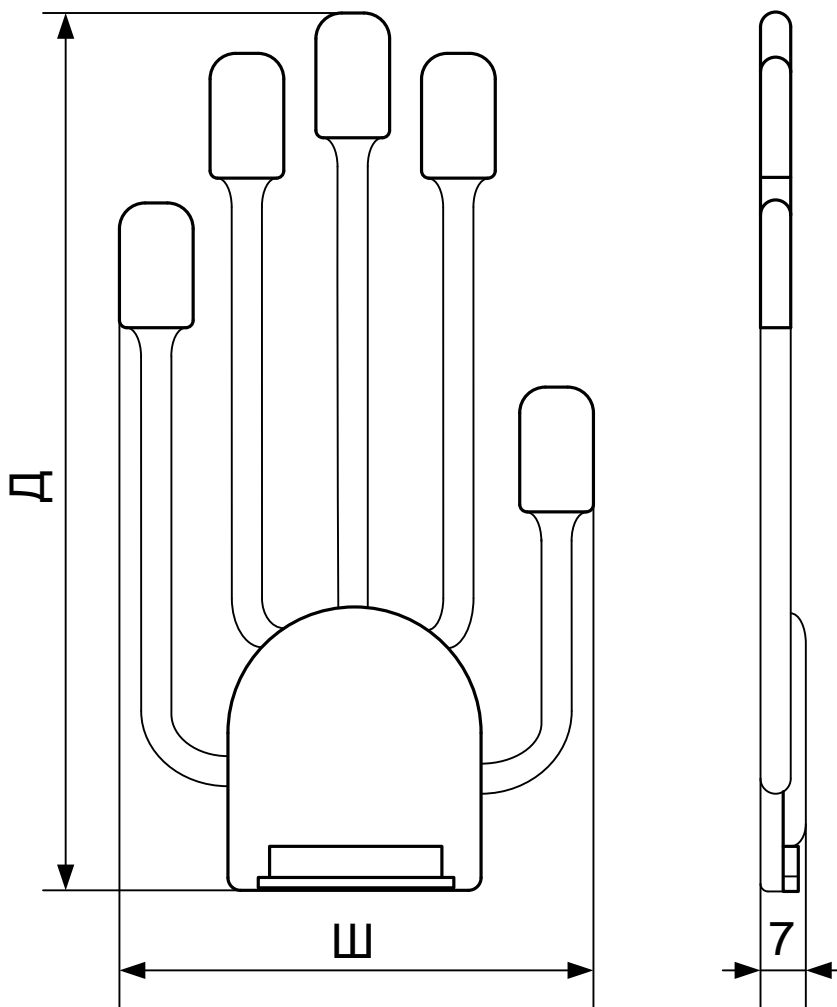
Габаритные размеры блока датчиков комплекса модификаций перчатка базовая и перчатка беспроводная
